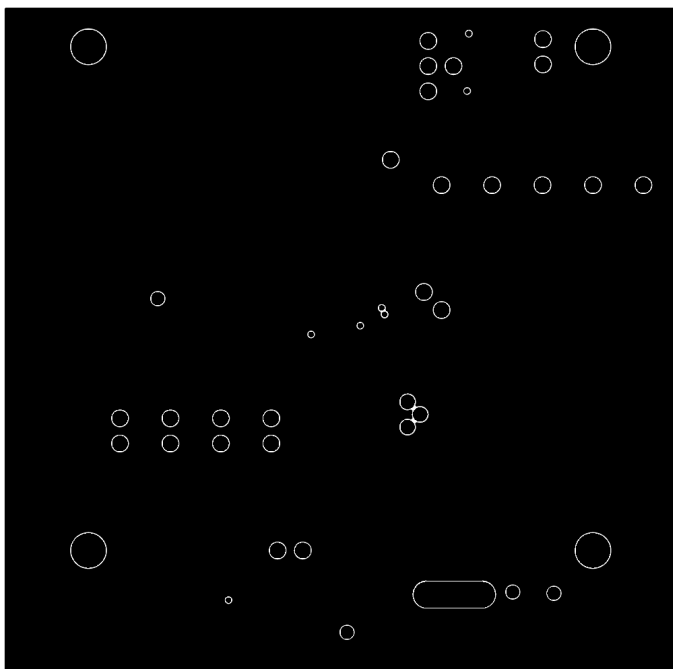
MAX3905 の EV キットの PCB レイアウト—グラウンドプレーン
